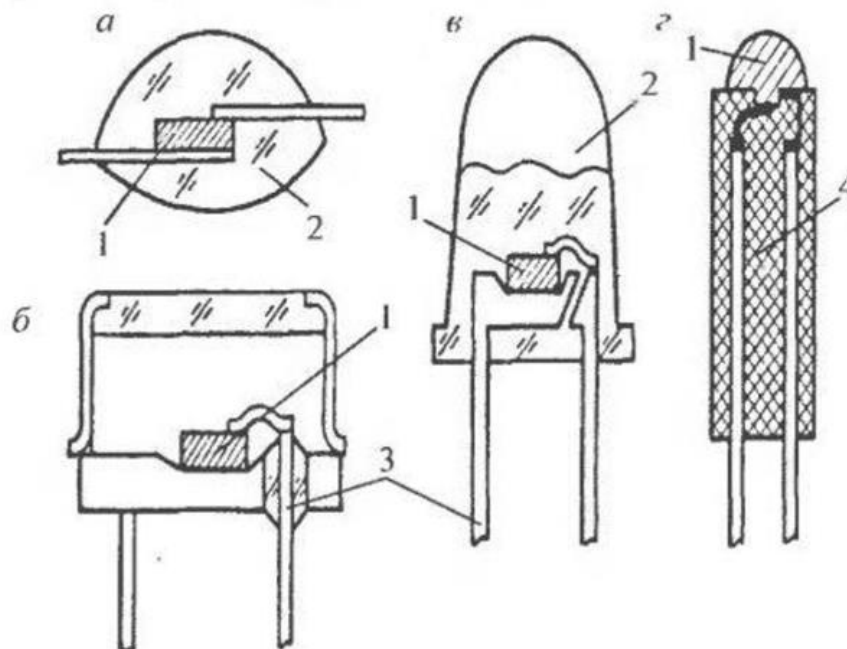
Конструкції деяких видів світлодіодів: а) безкорпусний; б) в металоскляному корпусі; в) з полімерною лінзою; г) у полімерному корпусі;
